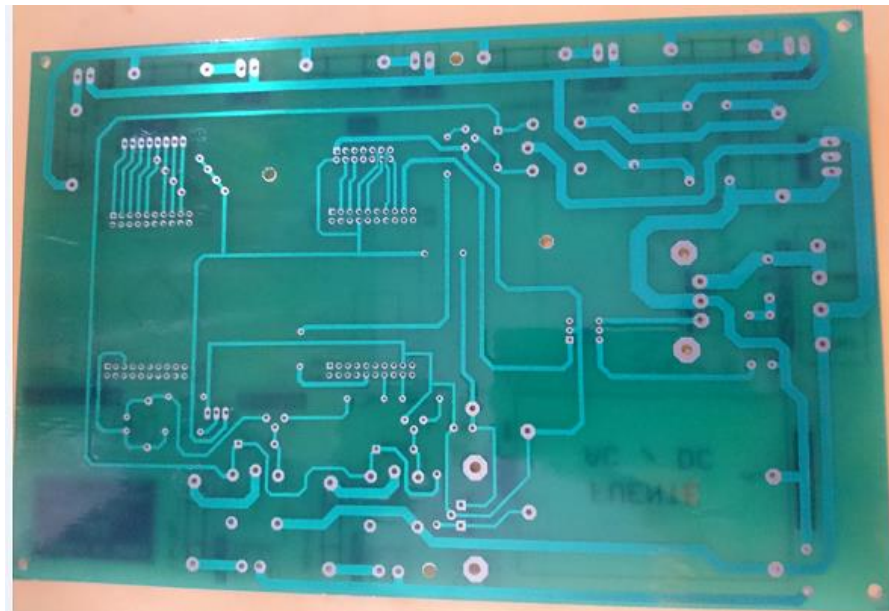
Vista inferior de placa de circuitos PCB interfaces construida.
